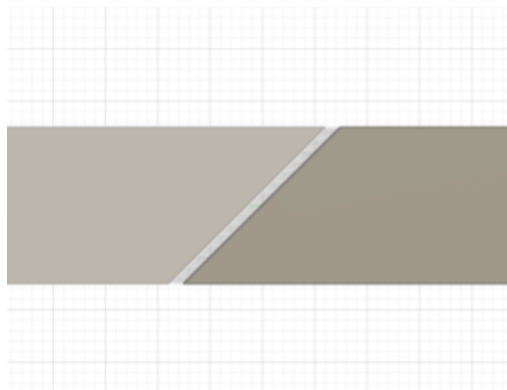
Dimensões do tubo do tipo 1 retiradas do desenho técnico.
